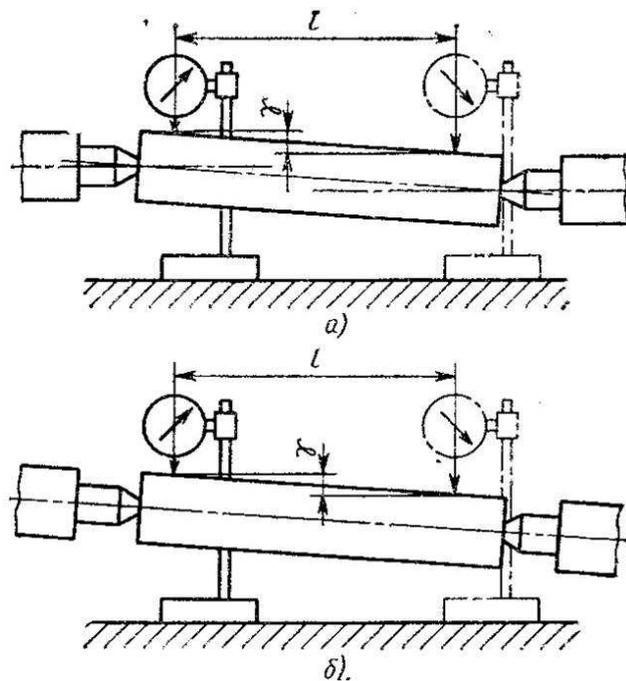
Проверка соосности центров токарного станка с помощью оправки:
